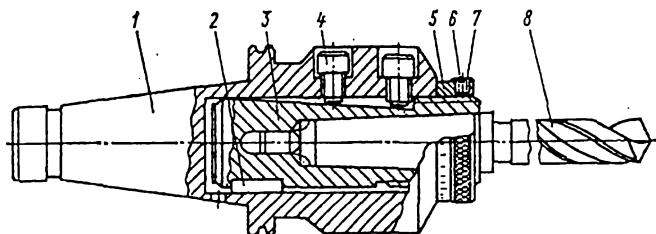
Збірний перехідний патрон для кріплення інструментів з конічним хвостовиком
